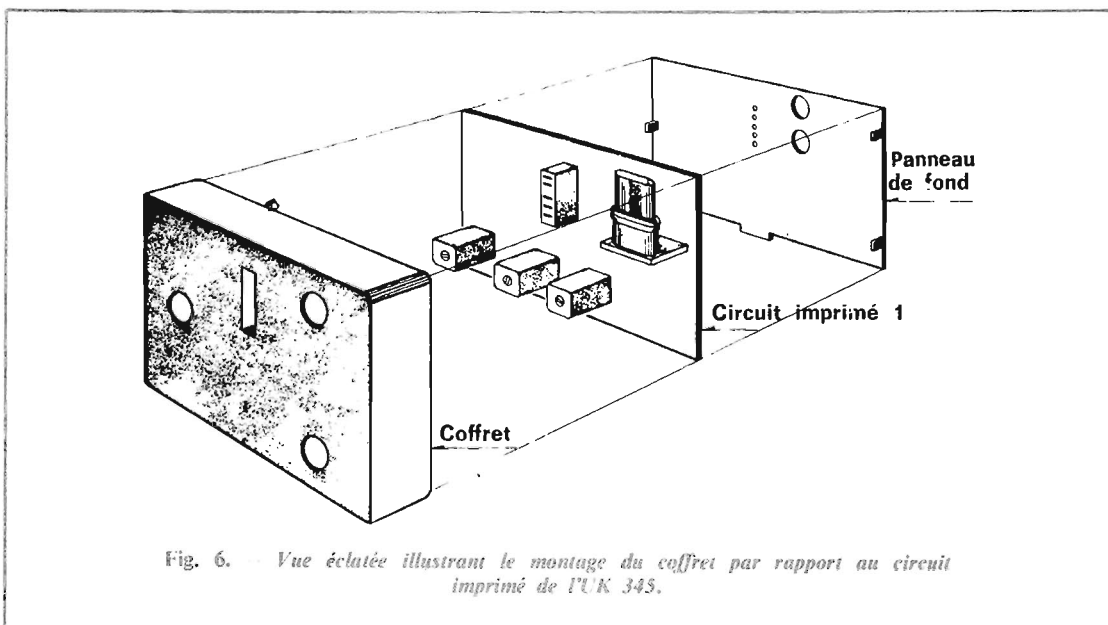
Vue éclatée illustrant le montage du coffret par rapport au circuit imprimé de l'UK 345.
